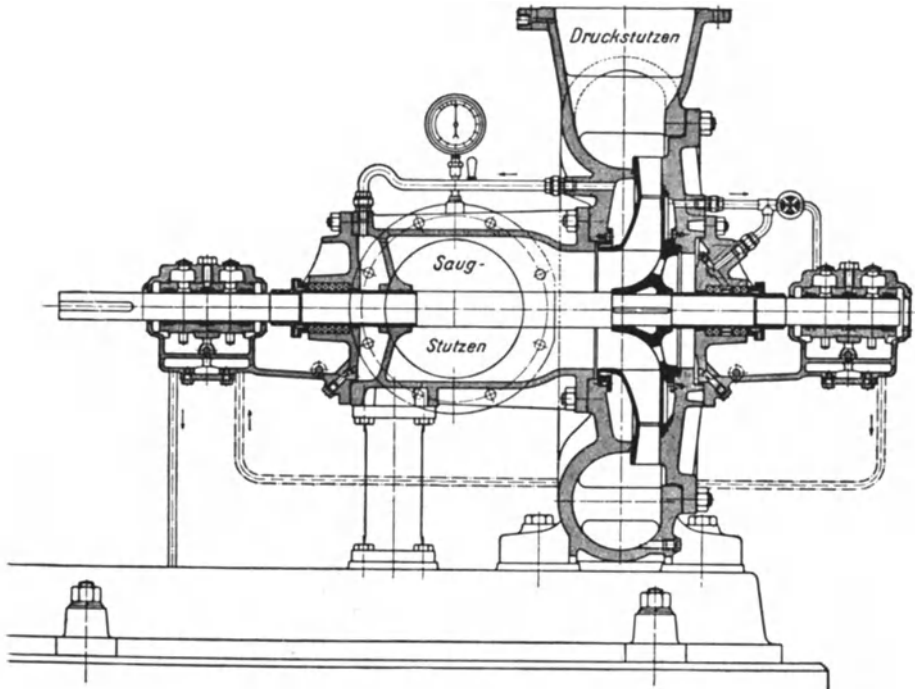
Einstufige Hochdruckpumpe (Borsig).
